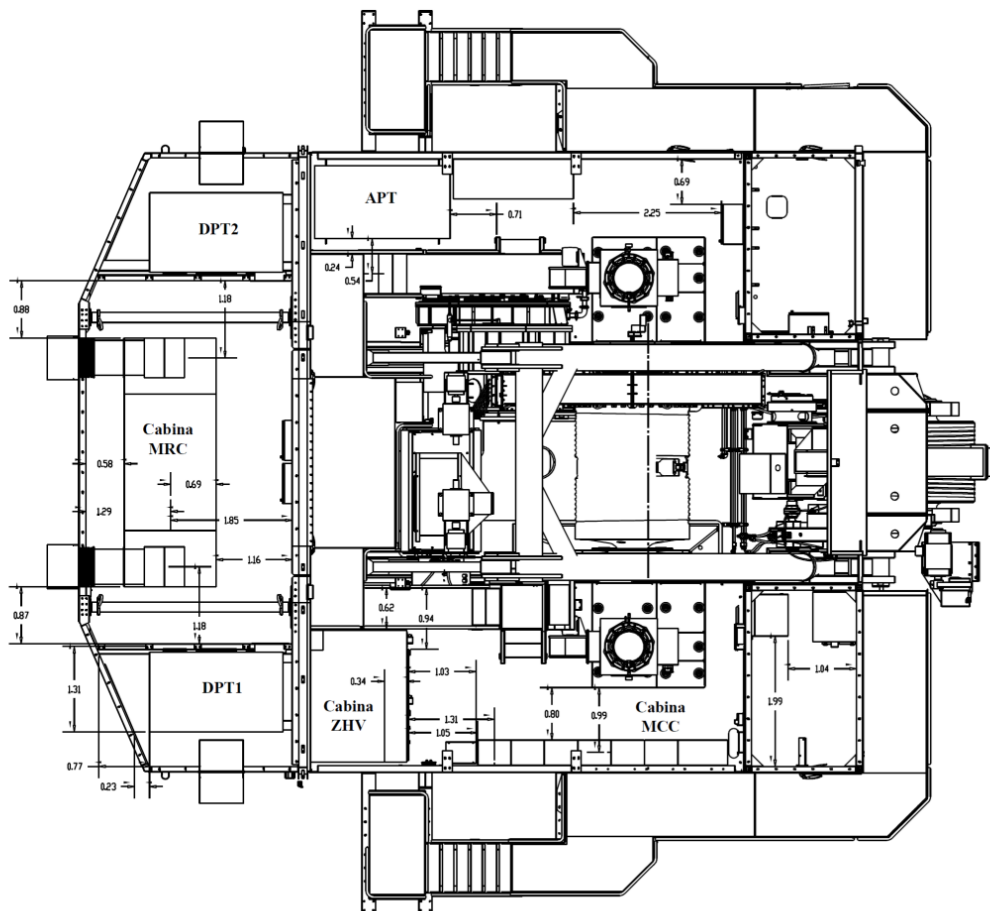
Levantamiento distancias de trabajo en cabinas eléctricas potencias en vista de planta de pala Bucyrus 495HR (dimensiones en metro)
